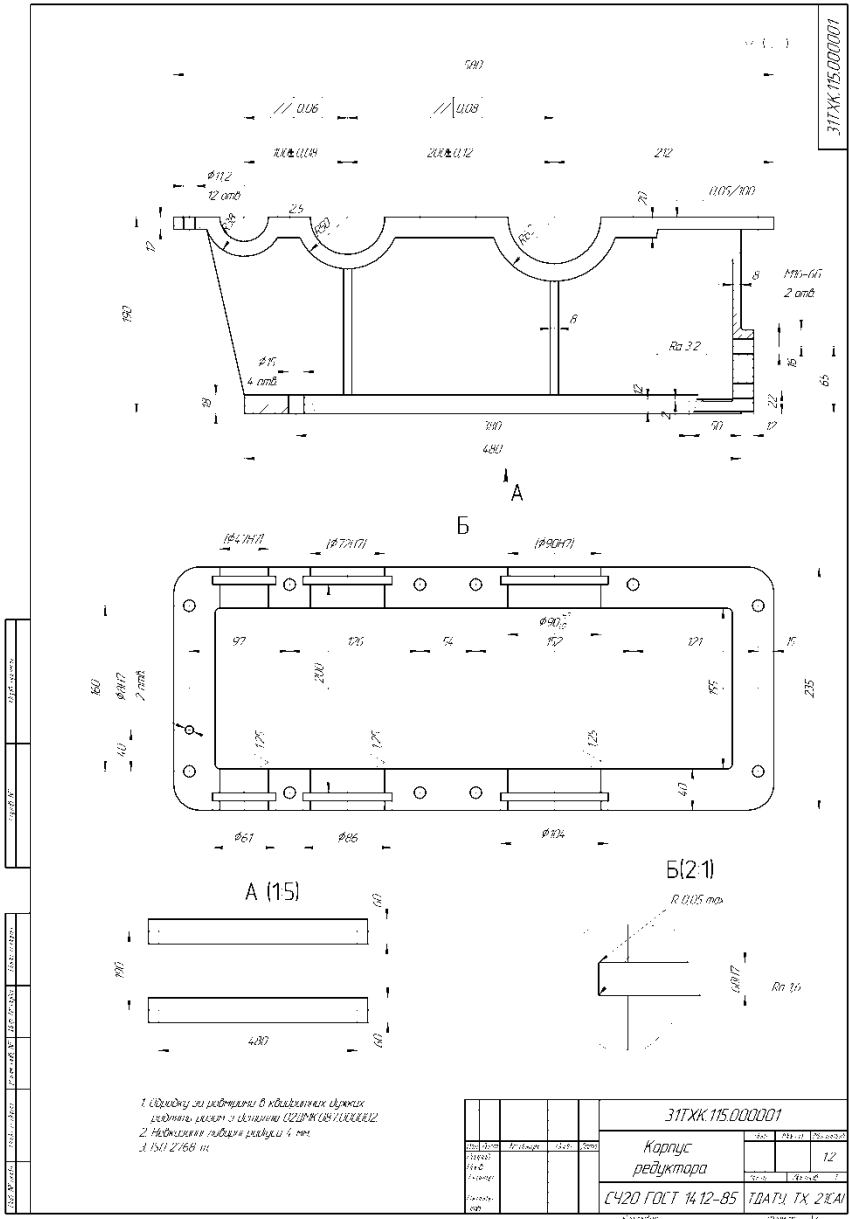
Приклад виконання робочого кресленника корпусу редуктора
